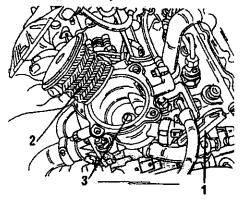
Снять подъемную скобу двигателя (1), топливный фильтр (2) и отвернуть болт (3).
